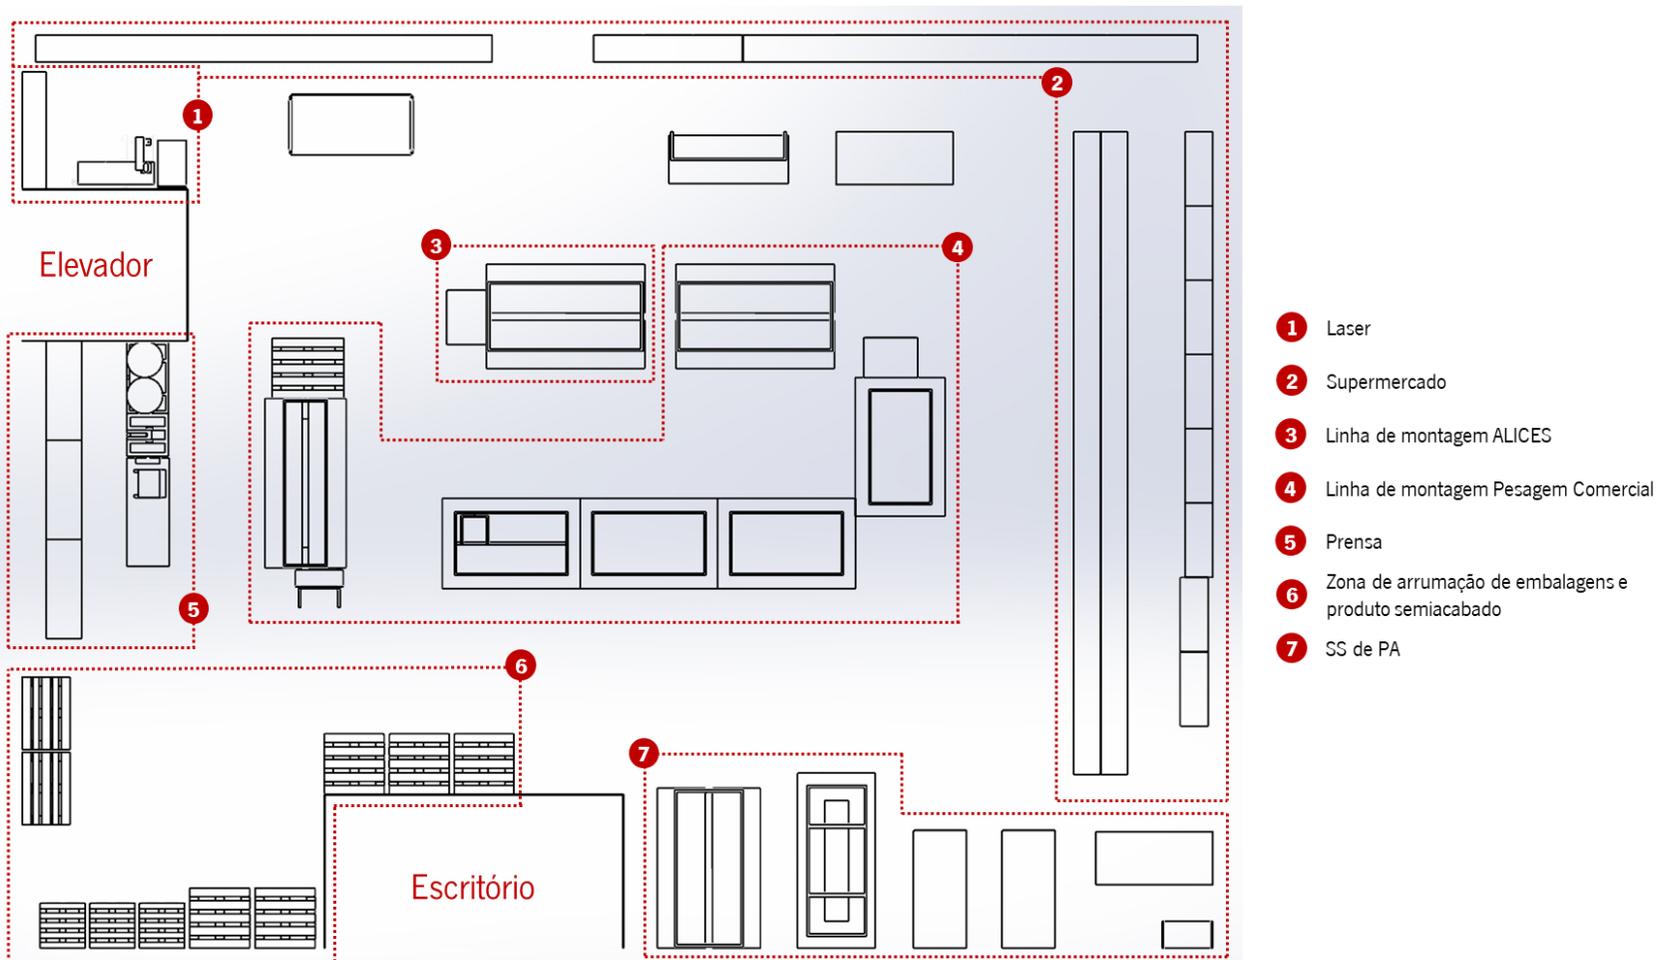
Layout 1D da Secção de Montagem Comercial - Vista de Cima (do autor)
